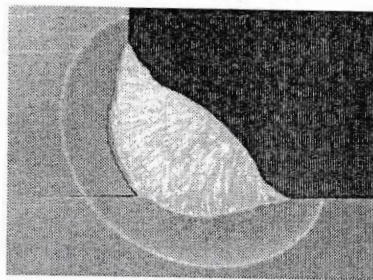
Fissuration dans la zone thermiquement affectée [I.7]
